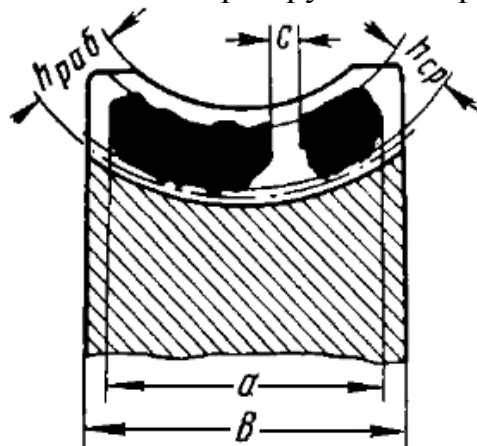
Пятно контакта витков червяка с зубом червячного колеса
